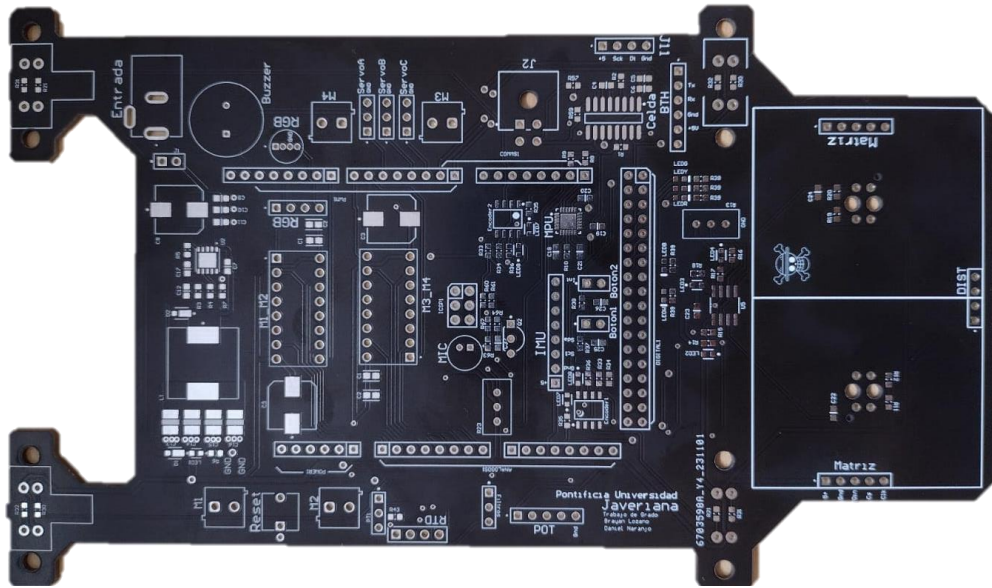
Vista superior del PCB fabricado versión 3 (Final)
